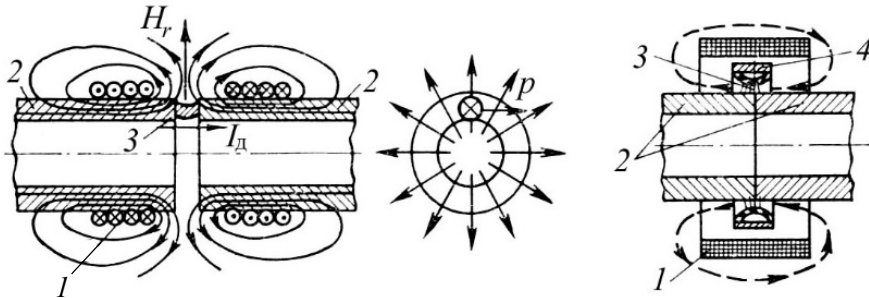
Схеми зварювання труб магнітокерованою дугою між крайками зварюваних труб (а) та між зварюваними трубами і допоміжним кільцевим неплавким електродом (б)
